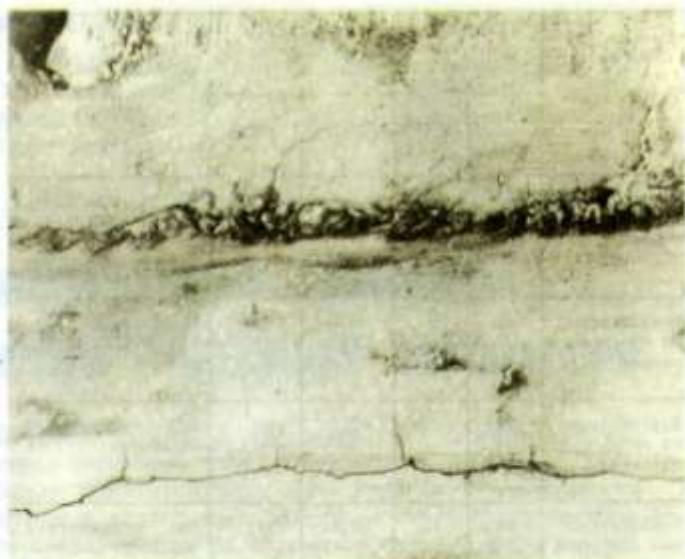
Трещины в зоне сплавления кольцевого сварного соединения
